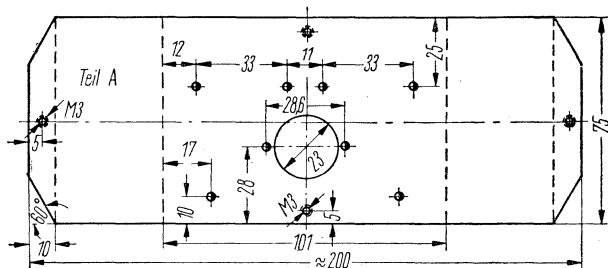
Maßskizze für das Chassis des 80-m-Konverters
